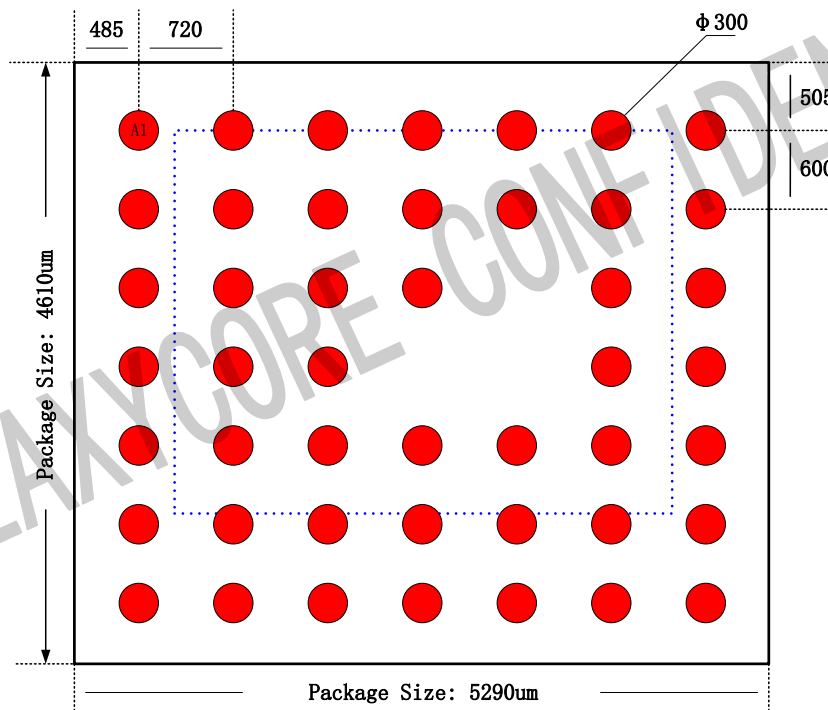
PCB 焊盘设计说明示意图(Top View)
